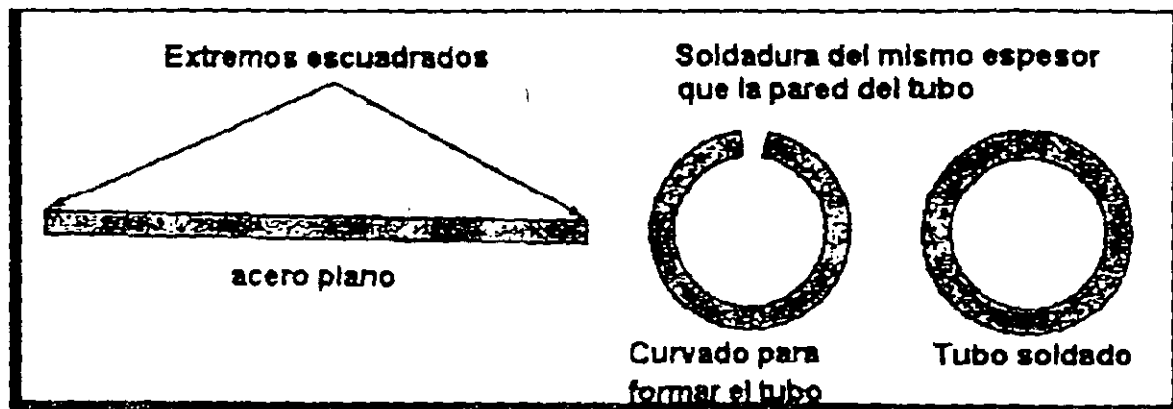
Esquema de fabricación de tubo soldado a tope
